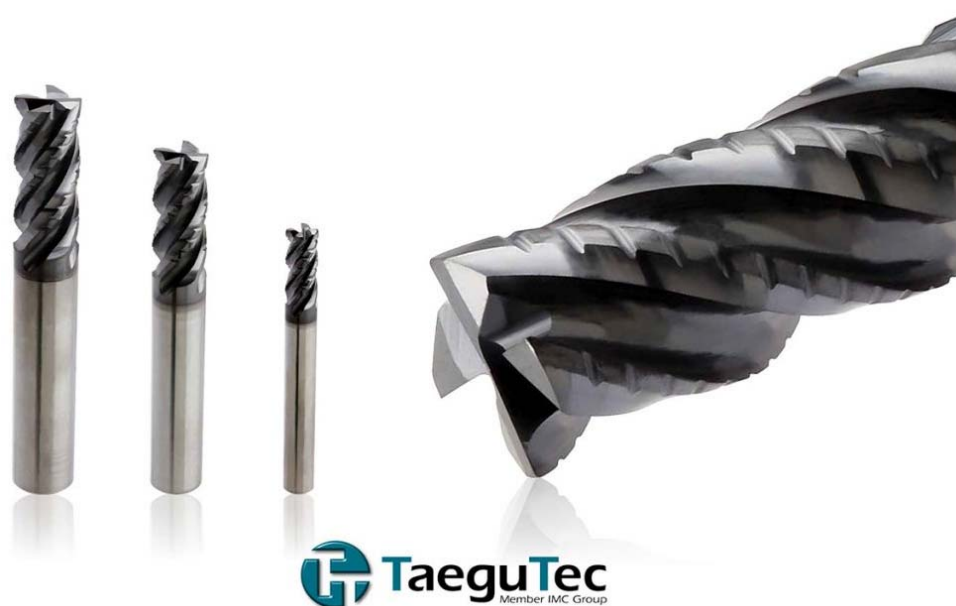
Черновые монолитные фрезы типа SER серии STARMILL с кромкой splitter
